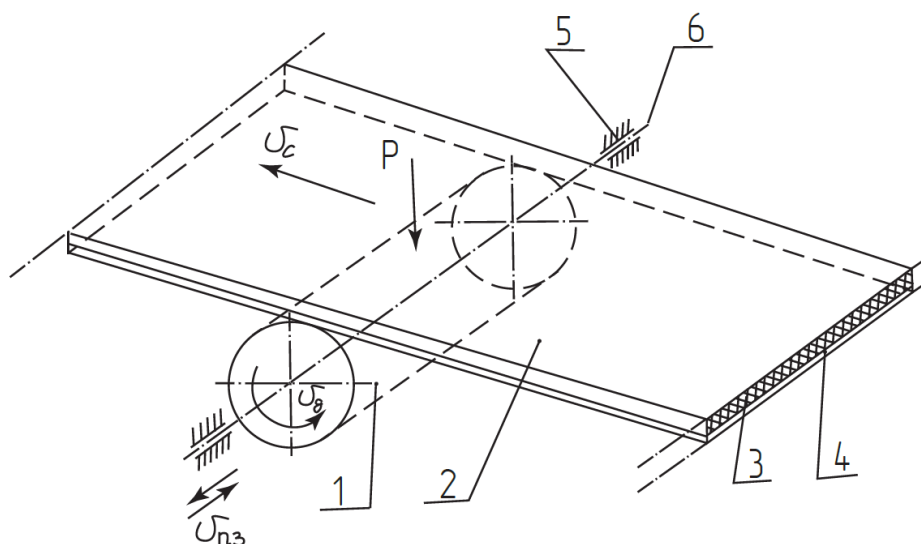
Схема полірування циліндричних поверхонь деталей алмазними стрічками
